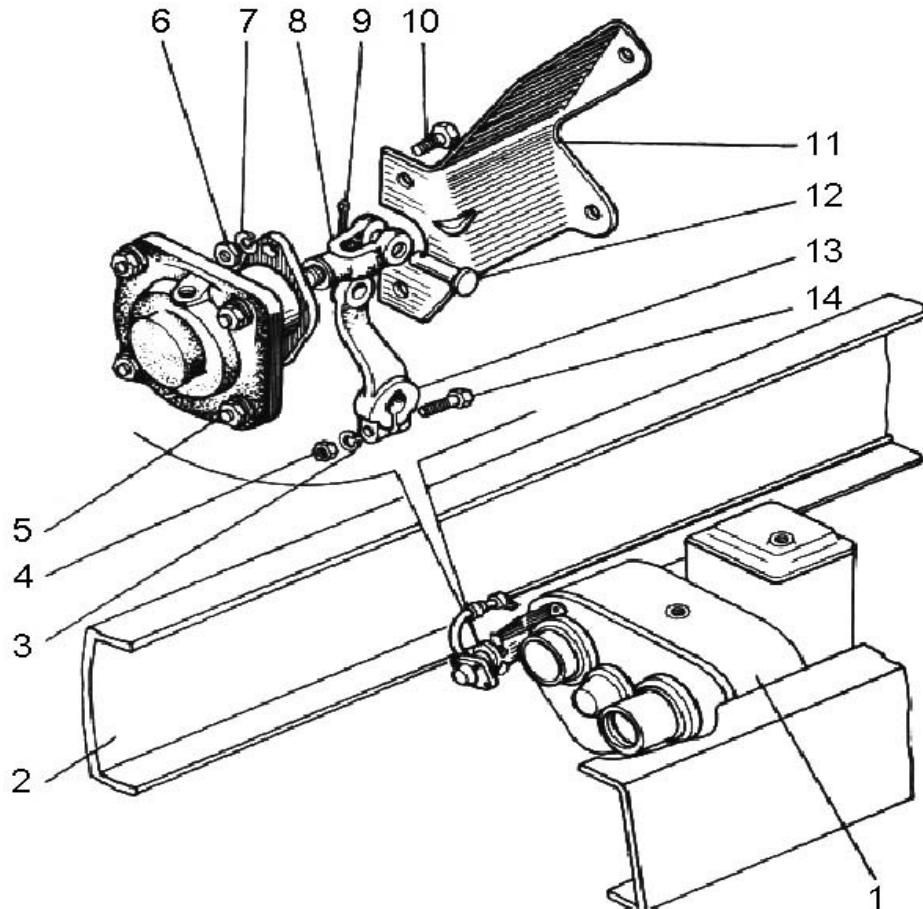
Установка пневмокамеры включения блокировки дифференциала:
